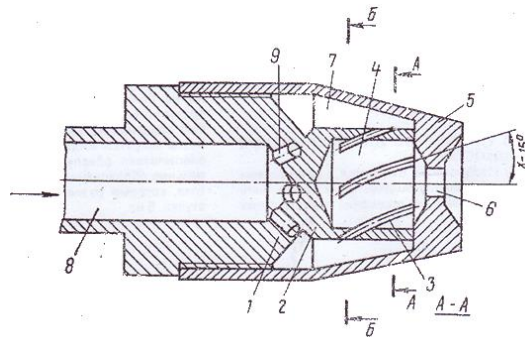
Розріз форсунки типу повний конус: 1– корпус; 2 – розпилювач; 3 – бокові пази; 4 – вихідний отвір; 5 – регулююча втулка; 6 – вихідний канал, 7 – порожнина, 8 – канал для подачі рідини, 9 – отвір подачі рідини
